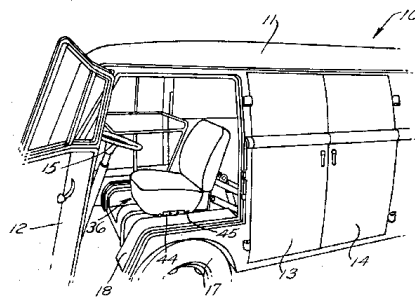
Vista en perspectiva de un furgón con la puerta abierta. (Patente nº US3236556 A, 1963).
